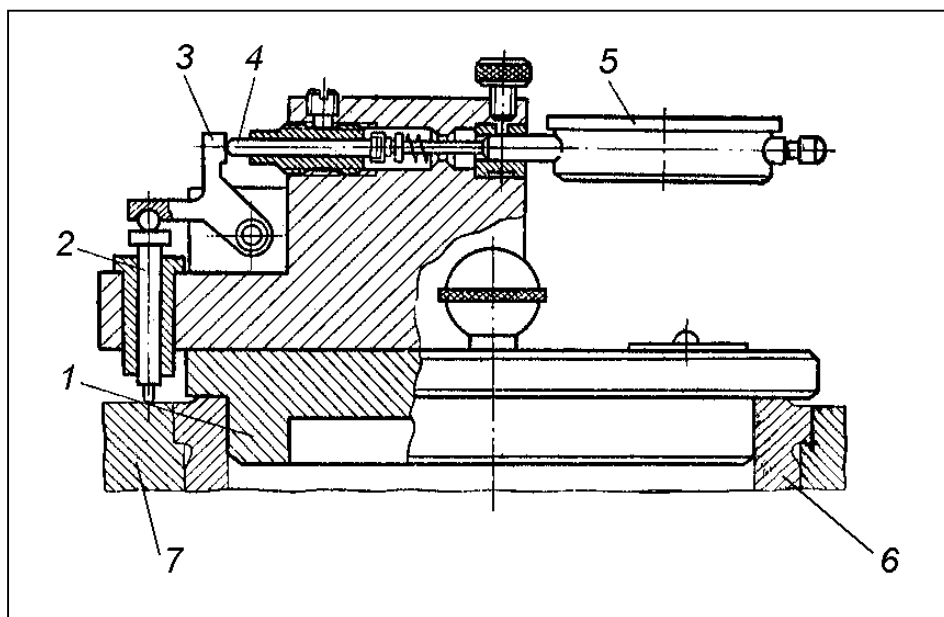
Приспособление для контроля выступа гильзы цилиндра:
